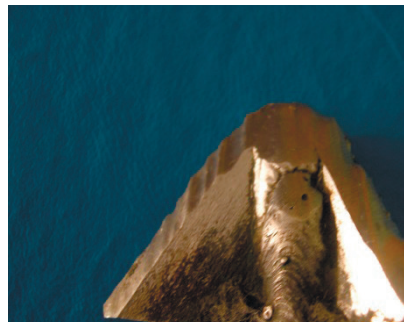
Сварная стрелчатая лапа с усилением в носовой части сварным швом
